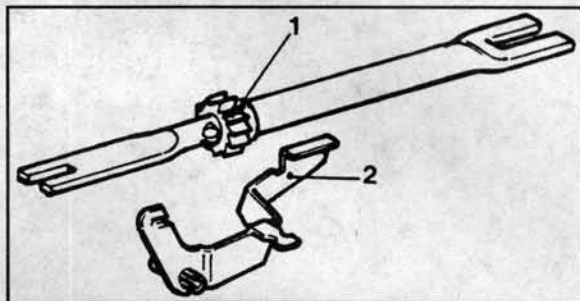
Механизм автоматической регулировки зазора барабанных тормозов автомобилей с двигателями В19 и В200
